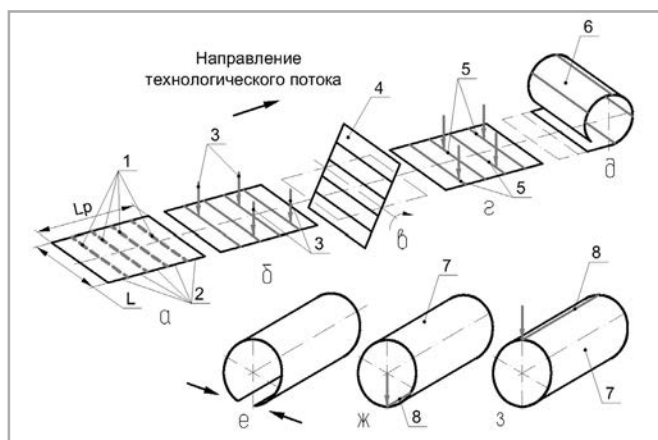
Схема технологического процесса изготовления обечайки из листового полотна: а – сборка полотна; б – автоматическая сварка первой стороны полотна; в – кантовка полотна на 180°; г – автоматическая сварка второй стороны; д – вальцовка обечайки; е – сборка замыкающего стыка обечайки; ж – автоматическая сварка внутреннего шва замыкающего стыка обечайки; з – автоматическая сварка наружного шва замыкающего стыка обечайки; 1 – сборочные сварные швы; 2 – листы полотна; 3 – сварочные автоматы; 4 – полотно в процессе кантовки; 5 – сварные швы полотна; 6 – полотно в процессе вальцовки; 7 – обечайка; 8 – замыкающий стык обечайки
